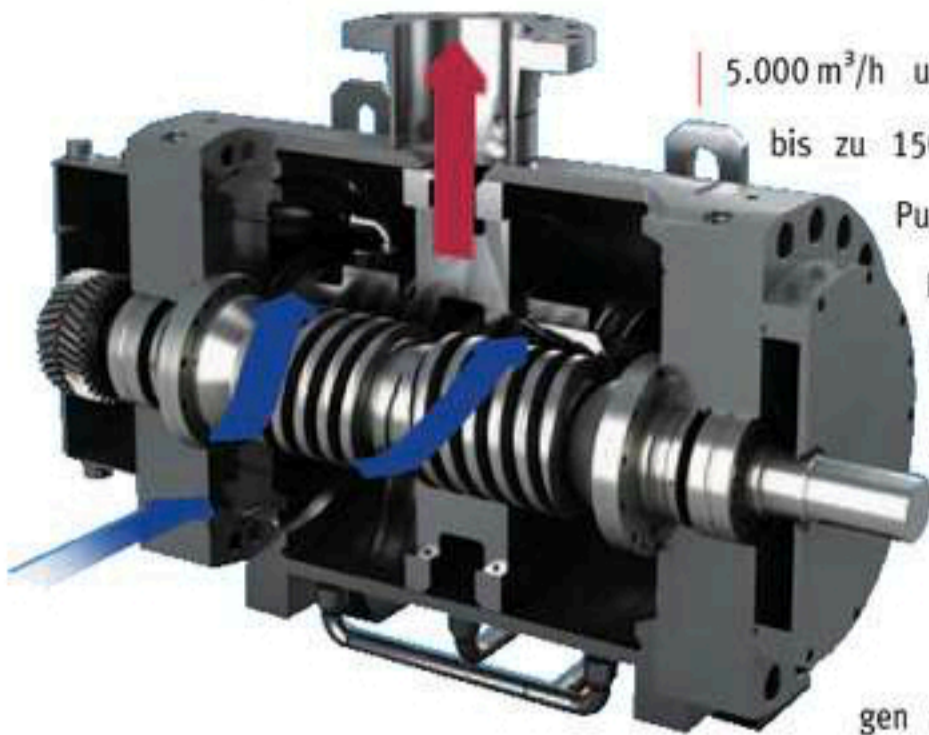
Innenansicht einer Hochdruck-Multiphasenpumpe
